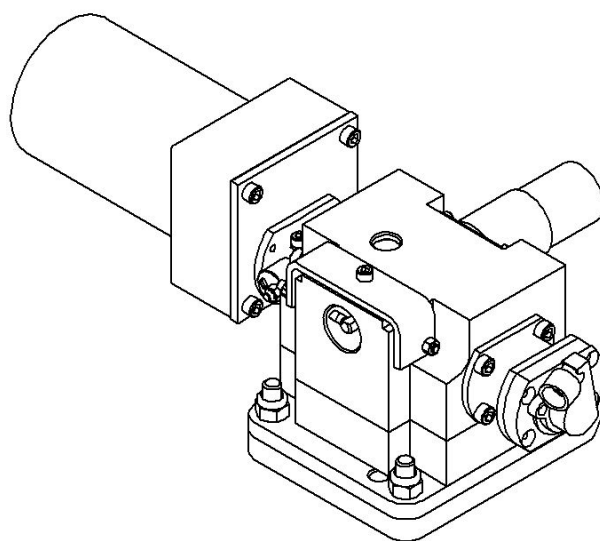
Загальний вид виконавчого пристрою механізму керування коробкою передач
